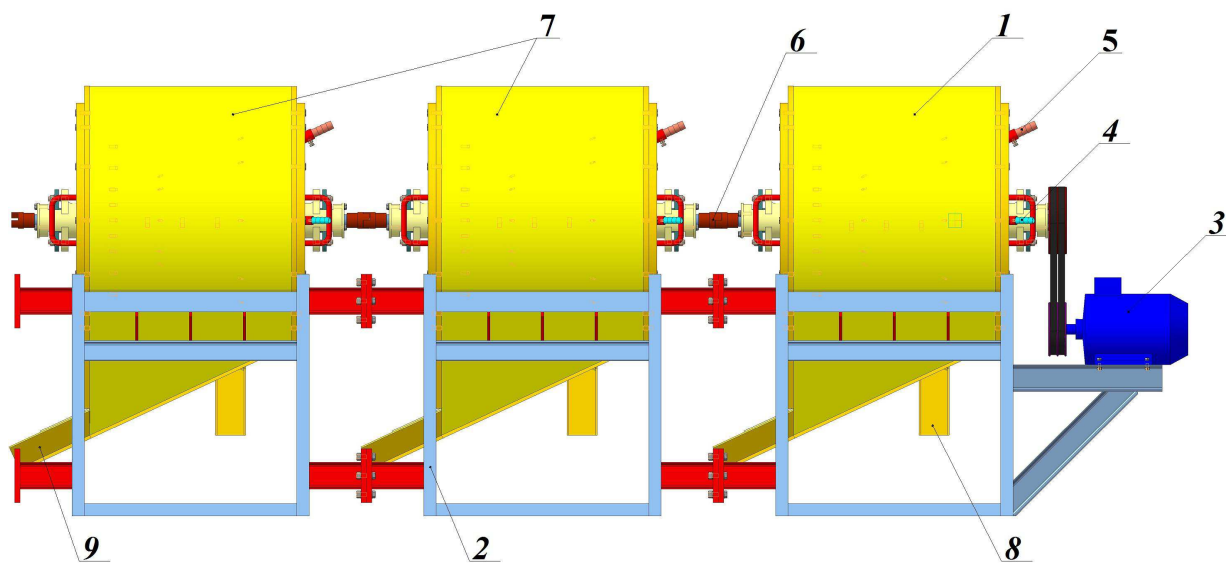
Трехмодульный центробежный сепаратор с непрерывной разгрузкой тяжелой фракции СЦ-600ГН:
